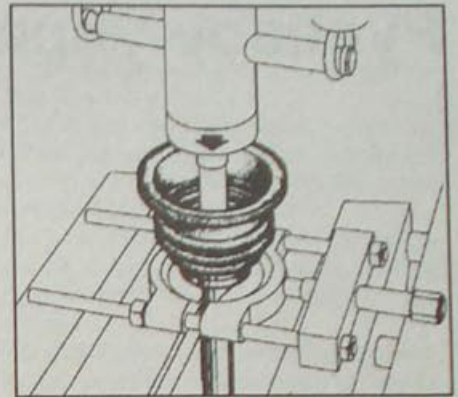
Использование прессы для выдавливания приводного вала из подшипника и защитного чехла
